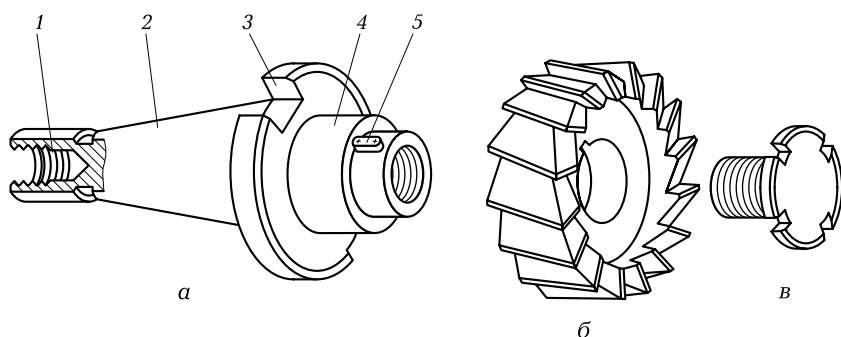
Концевая оправка (*а*), торцевая насадная фреза (*б*) и крепежный винт (*в*):
